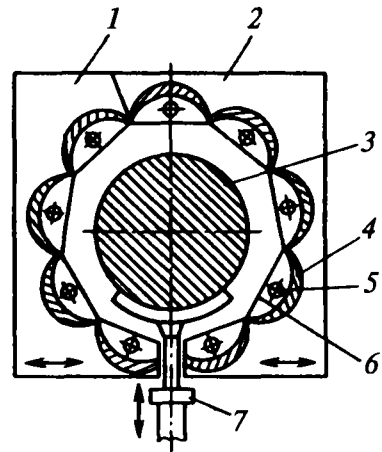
Мощная отражательная печь для нагрева заготовок под ковку: 1, 2 — раздвижные блоки печи; 3 — нагреваемая заготовка; 4 — параболический отражатель; 5 — ГЛН; 6 — кварцевое окно; 7 — пневмоцилиндр подъема и опускания заготовок
